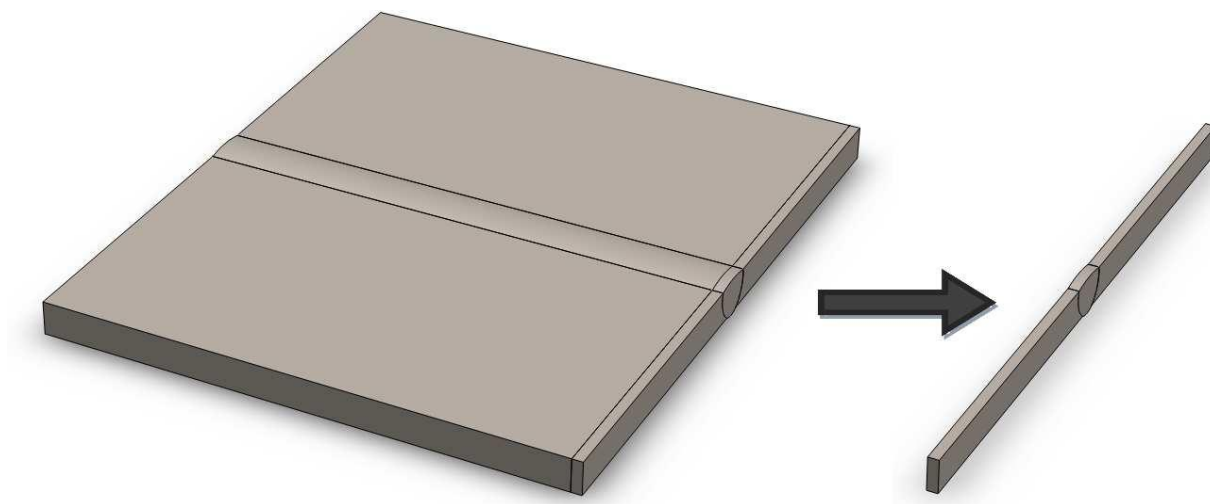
Изготовление плоских образцов стыкового соединения
